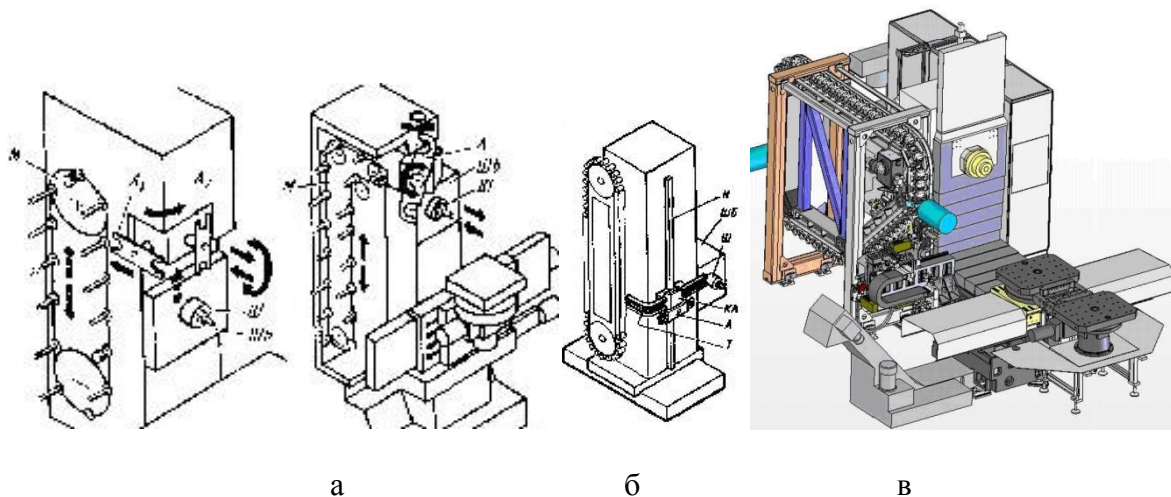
Устройства АСИ при боковом расположении магазина на горизонтальных МС
